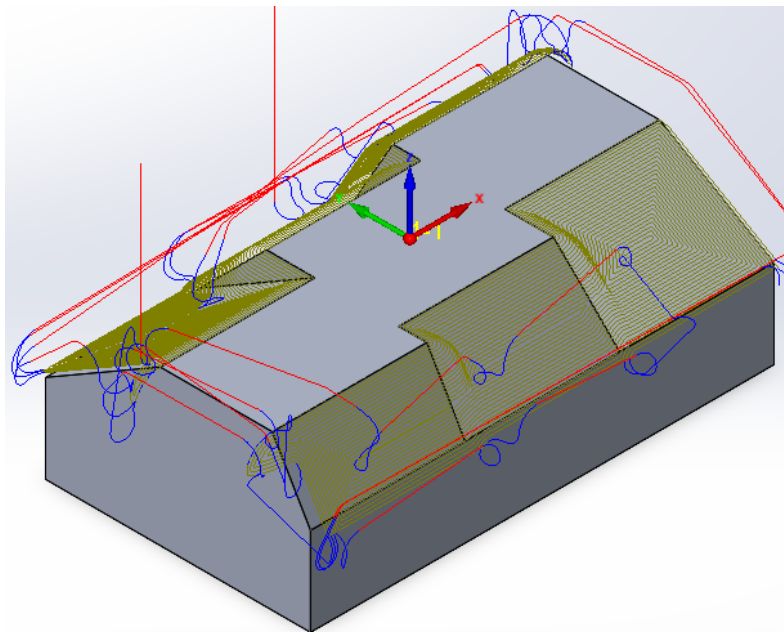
Trajetória executada durante a operação de maquinação de passagem constante 3D
